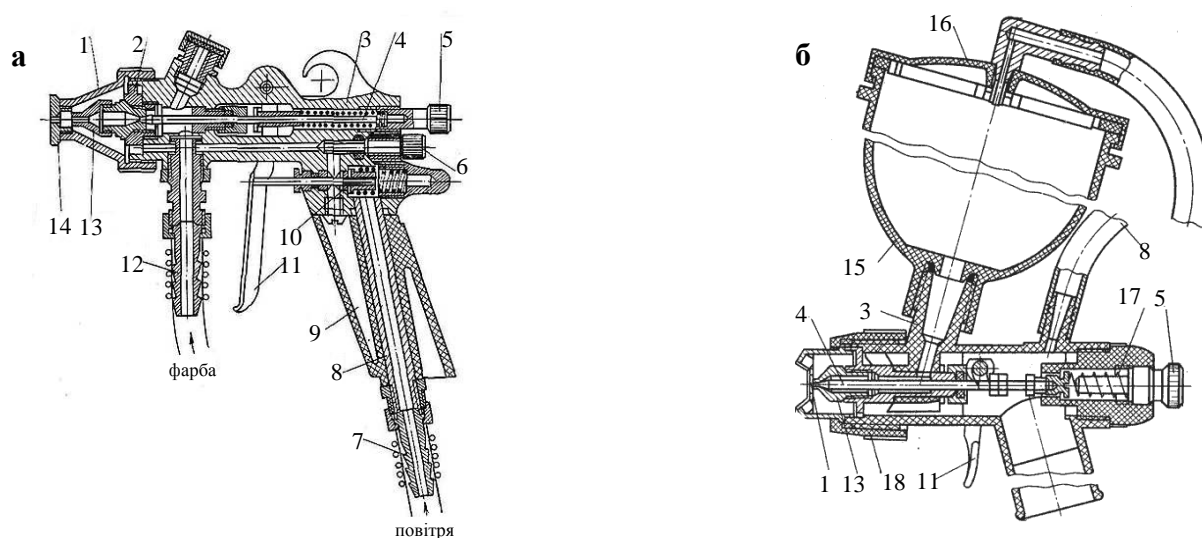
Схема фарборозпилювача: а – автоматичний; б – механічний; 1 – головка; 2 – штуцер; 3 – корпус; 4 – голка; 5 – регулятор голки; 6 – регулятор повітря; 7 – ніпель; 8 – трубка для повітря; 9 – ручка; 10 – курок; 11 – повітряний клапан; 12 – ніпель для фарби; 13 – сопло; 14 – змінне наконеччя; 15 – бачок; 16 – кришка; 17 – пружина; 18 – гайка накидна
